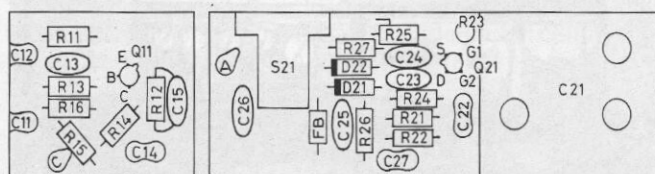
Disposición de componentes en las placas del detector (izquierda) y oscilador (derecha).
